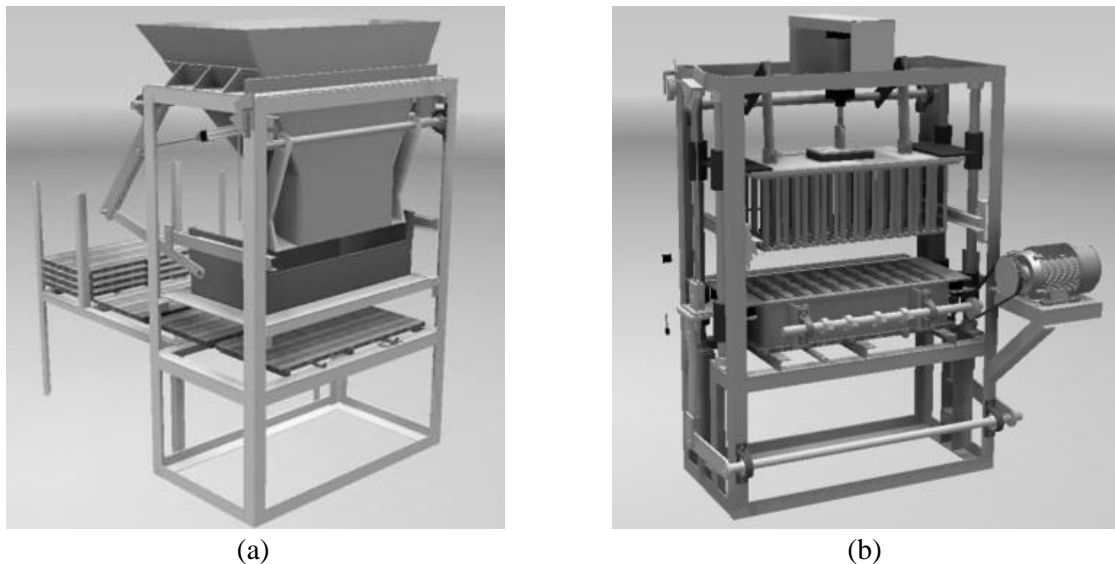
Módulos de la máquina: (a) suministro de concreto y (b) fabricación.
